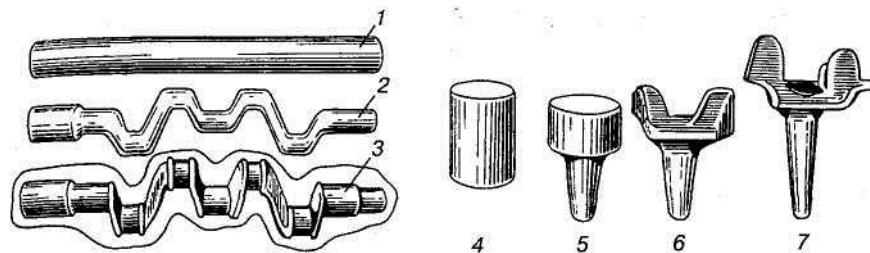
Послідовність переходів при штампуванні на пресі колінчастого валу та поворотного кулака автомобіля: 1 – круглий прокат, 2 – зігнута заготовка, 3 – штампована заготовка з облоєм, 4 – заготовка, 5, 6, 7 – послідовні переходи
